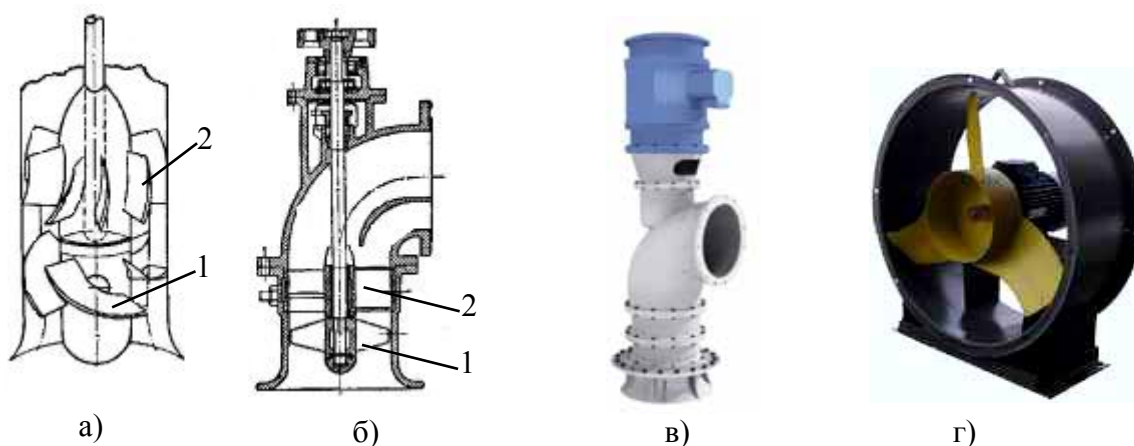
Конструкція (а, б) та зовнішній вигляд осьового насоса (v) та вентилятора (г): 1 – робоче колесо; 2 – напрямний апарат
